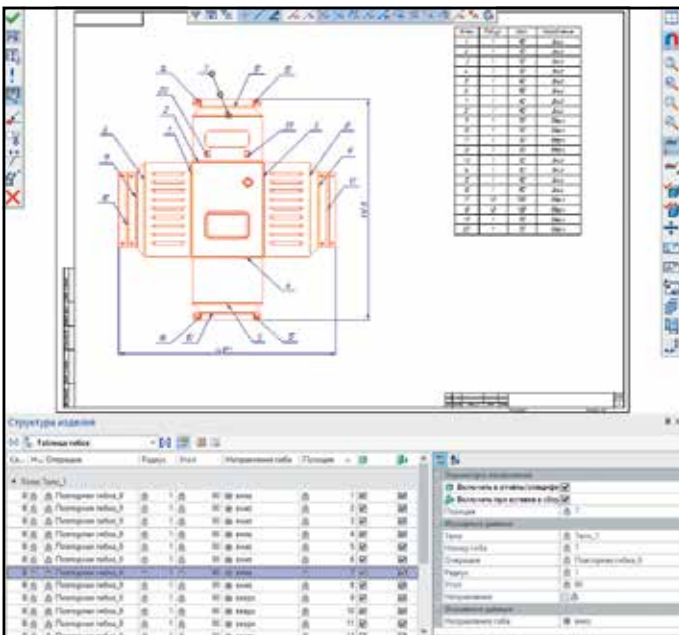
Развертка листовой детали с номерами гибов и таблицей сгибов
